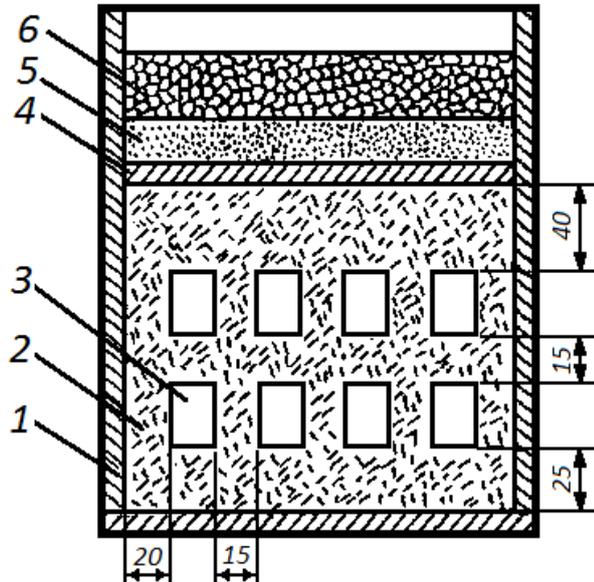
Схема упаковки контейнера с плавким затвором:
